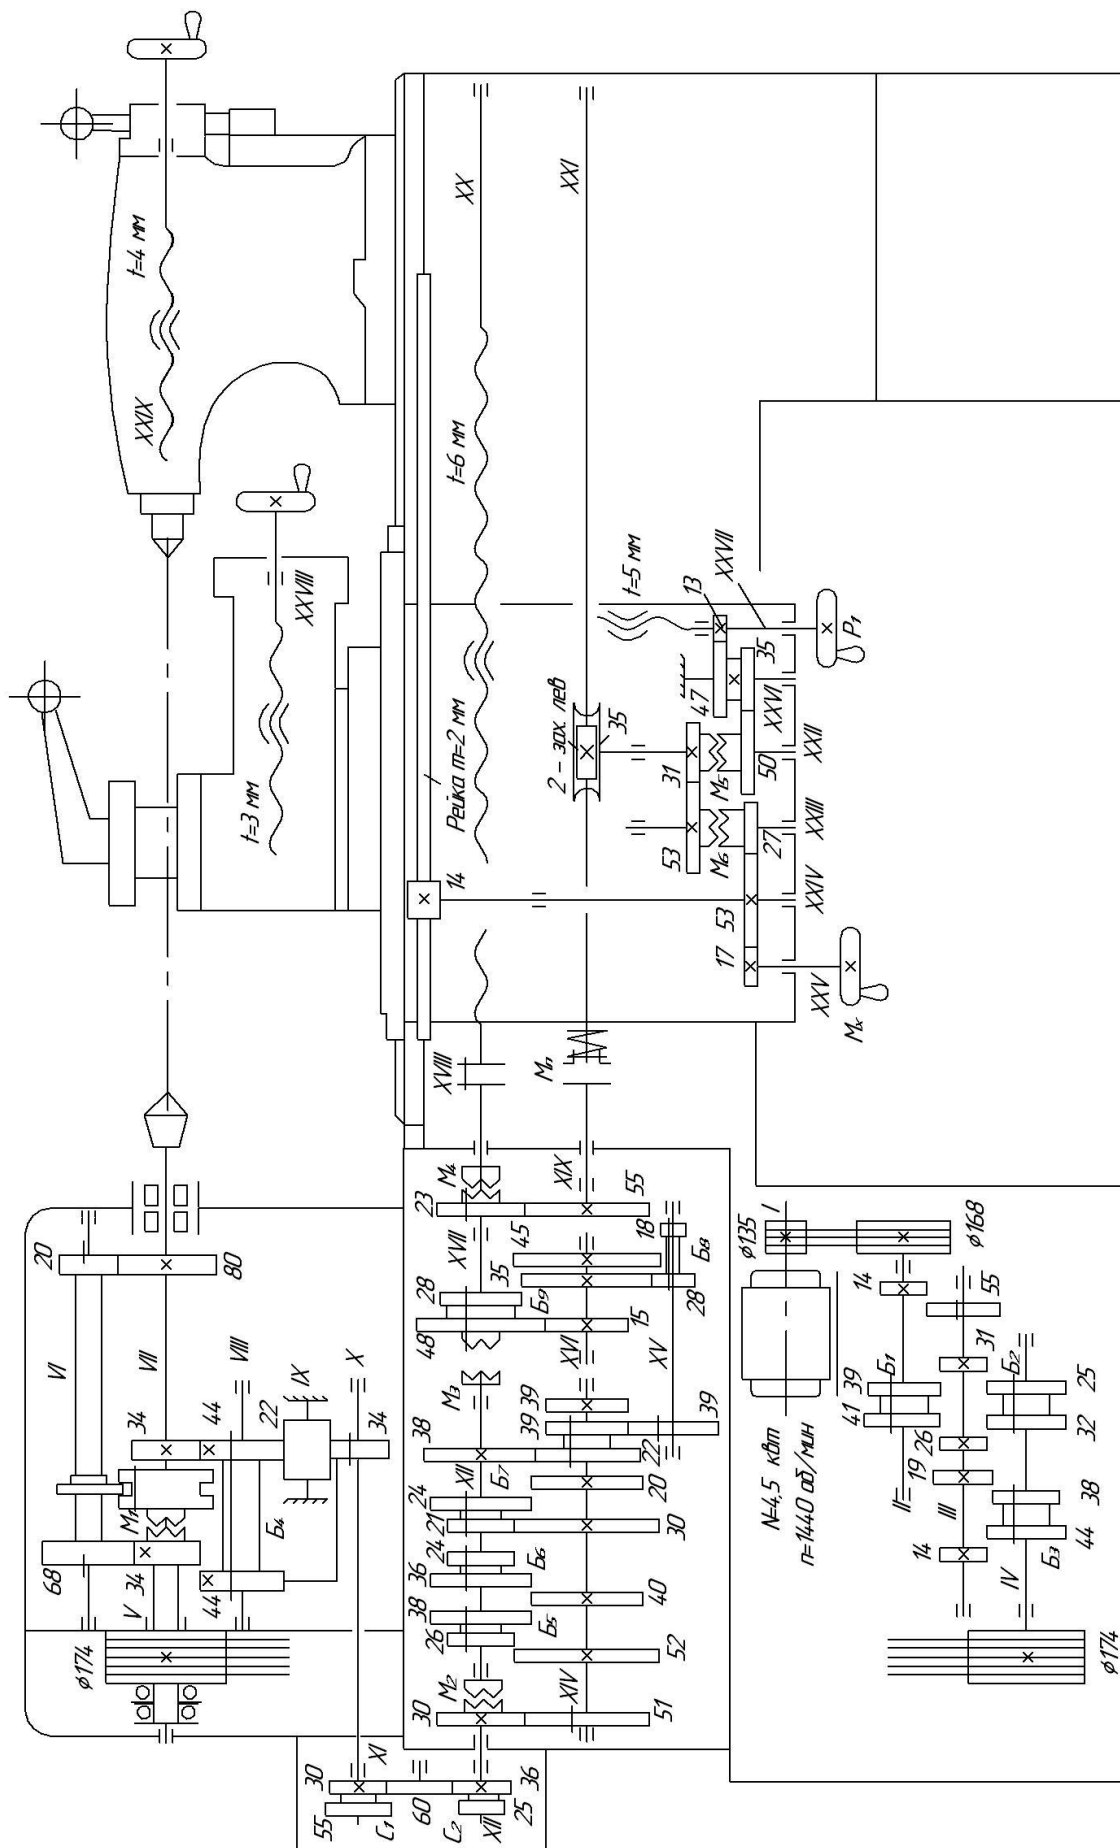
Кинематическая схема токарно-винторезного станка 1А616
